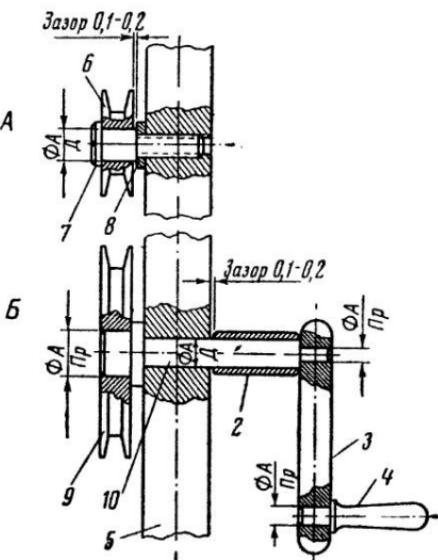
Модель клиноременной передачи (схема соединения деталей): А — узел ведомого шкива (6 — ведомый шкив, 7 — ось ведомого шкива, 8 — шайба); Б — узел привода (2 — упорная втулка, 3 — рычаг, 4 — ручка, 5 — стойка, 9 — ведущий шкив, 10 — ведущий вал).
